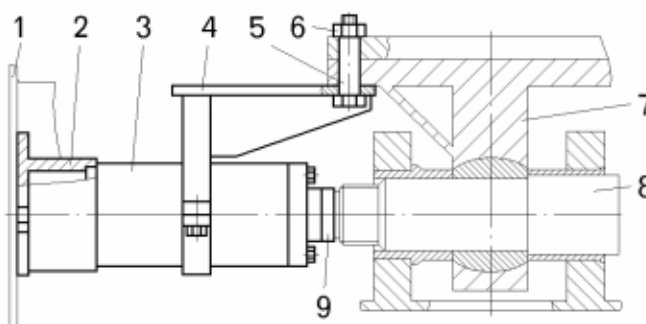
Приспособление для выпрессовки центрального пальца задней подвески:
